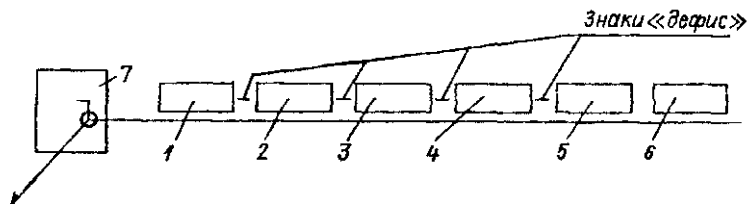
Структура условного обозначения стандартного сварного шва
